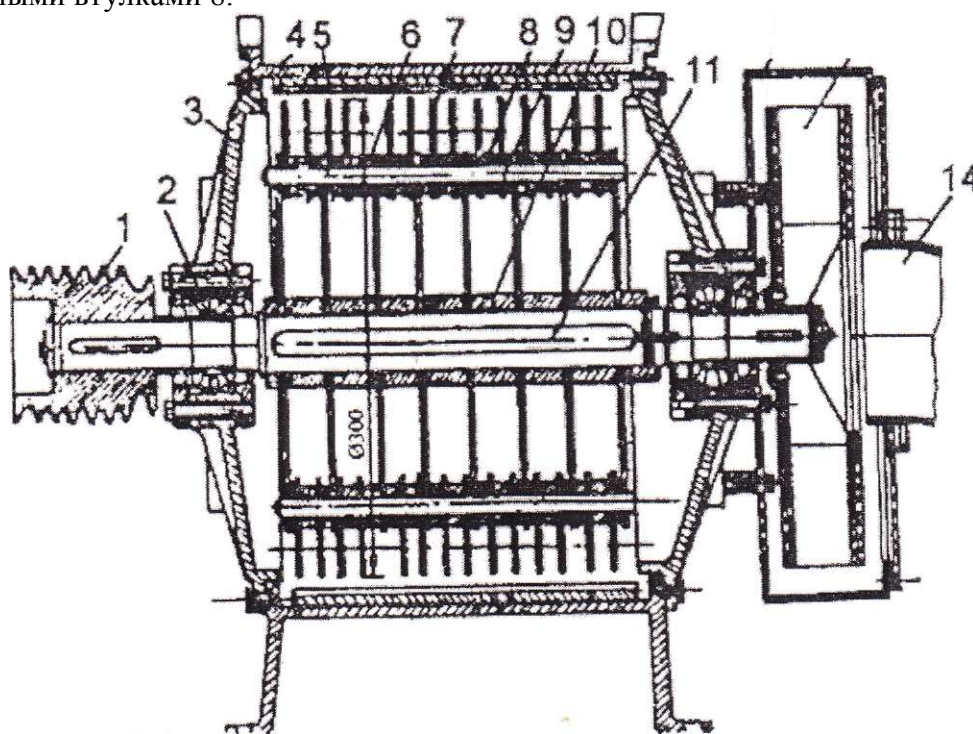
Молотковый барабан КДУ-2А с вентилятором:
